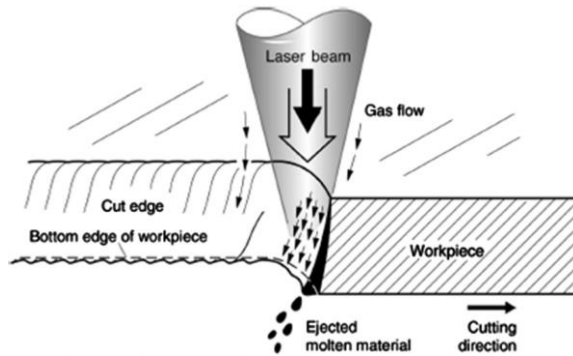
Esquema del corte por láser. Fuente: *CO₂ Laser Cutting; Powell John [11]
